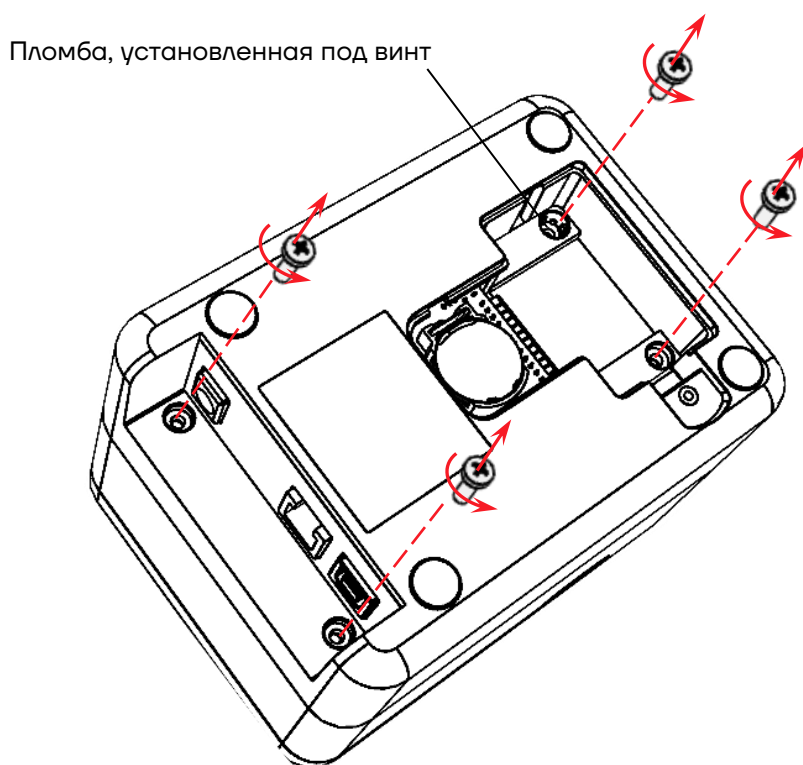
Винты крепления нижней части корпуса к верхней части
